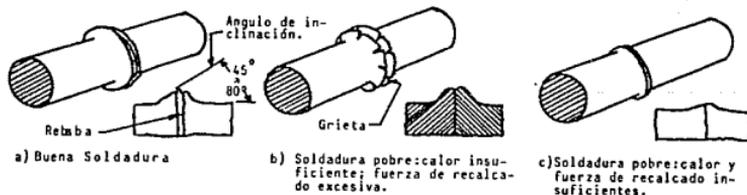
Formas de recalado de soldadura que indican la calidad de la soldadura y adecuación de calor y fuerza de recalado usados durante la soldadura.
